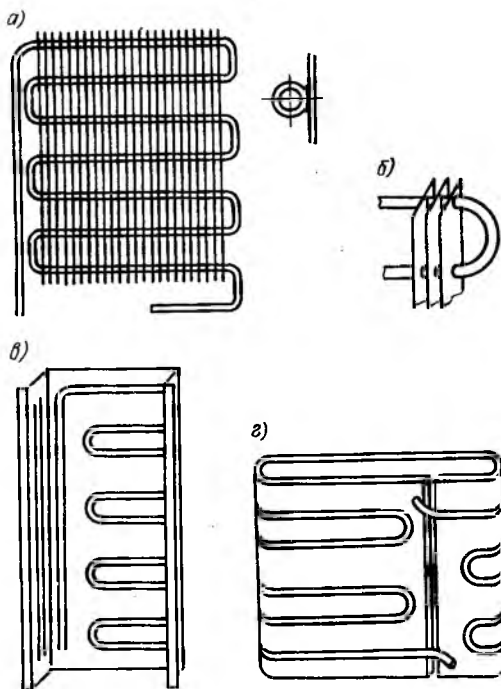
Конденсаторы домашних холодильных шкафов; а — с проволочным оребрением; б — фрагмент конденсатора с плоскими ребрами; в — конденсатор трубчатый с листовым оребрением; г — конденсатор листотрубный прокатно-сварной
